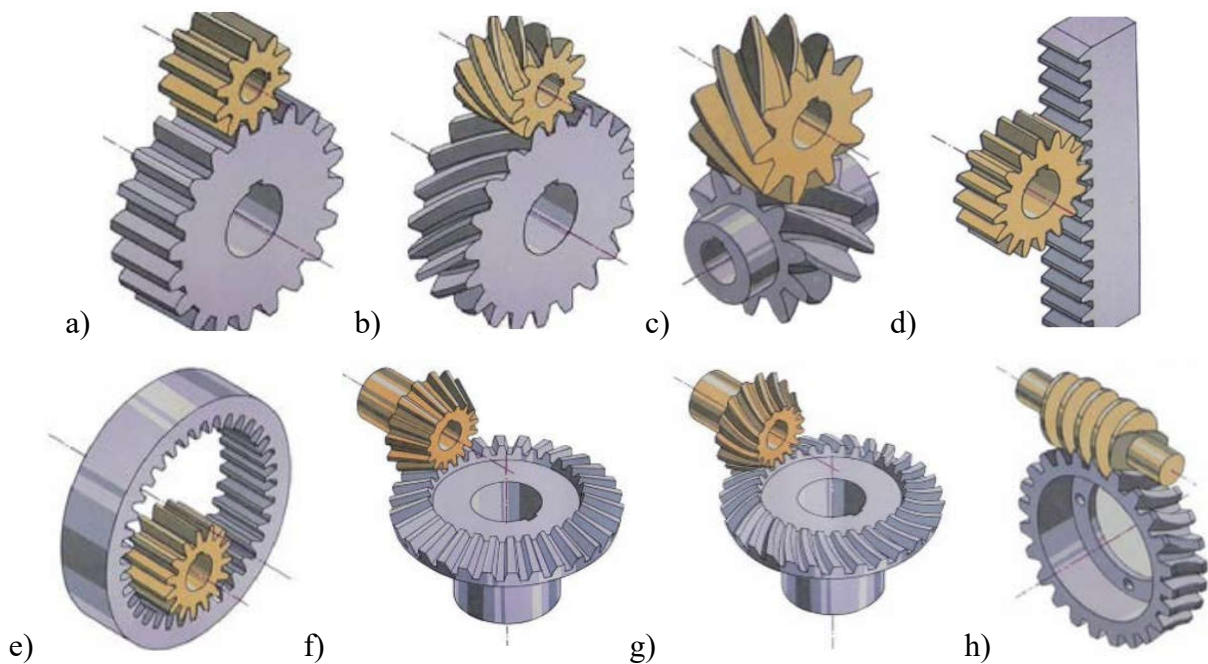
Types d'engrenages : a - engrenage droit ; b - cylindrique hélicoïdal ; c - chevron cylindrique ; d - crémaillère ; e - cylindrique à denture interne ; f - engrenage conique ; g - hélicoïdal conique ; h - vis sans fin
